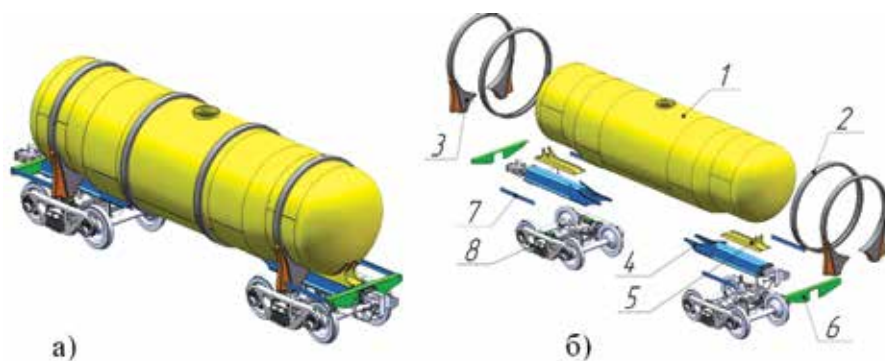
Инновационный вагон-цистерна для перевозки серной кислоты: а) – общий вид конструкции вагона; б) разнесенный вид вагона: 1 – котел; 2 – шпангоут; 3 – шпангоут, совмещенный с опорами; 4 – хребтовая балка; 5 – опора котла; 6 – лобовая балка; 7 – продольная балка; 8 – тележка
